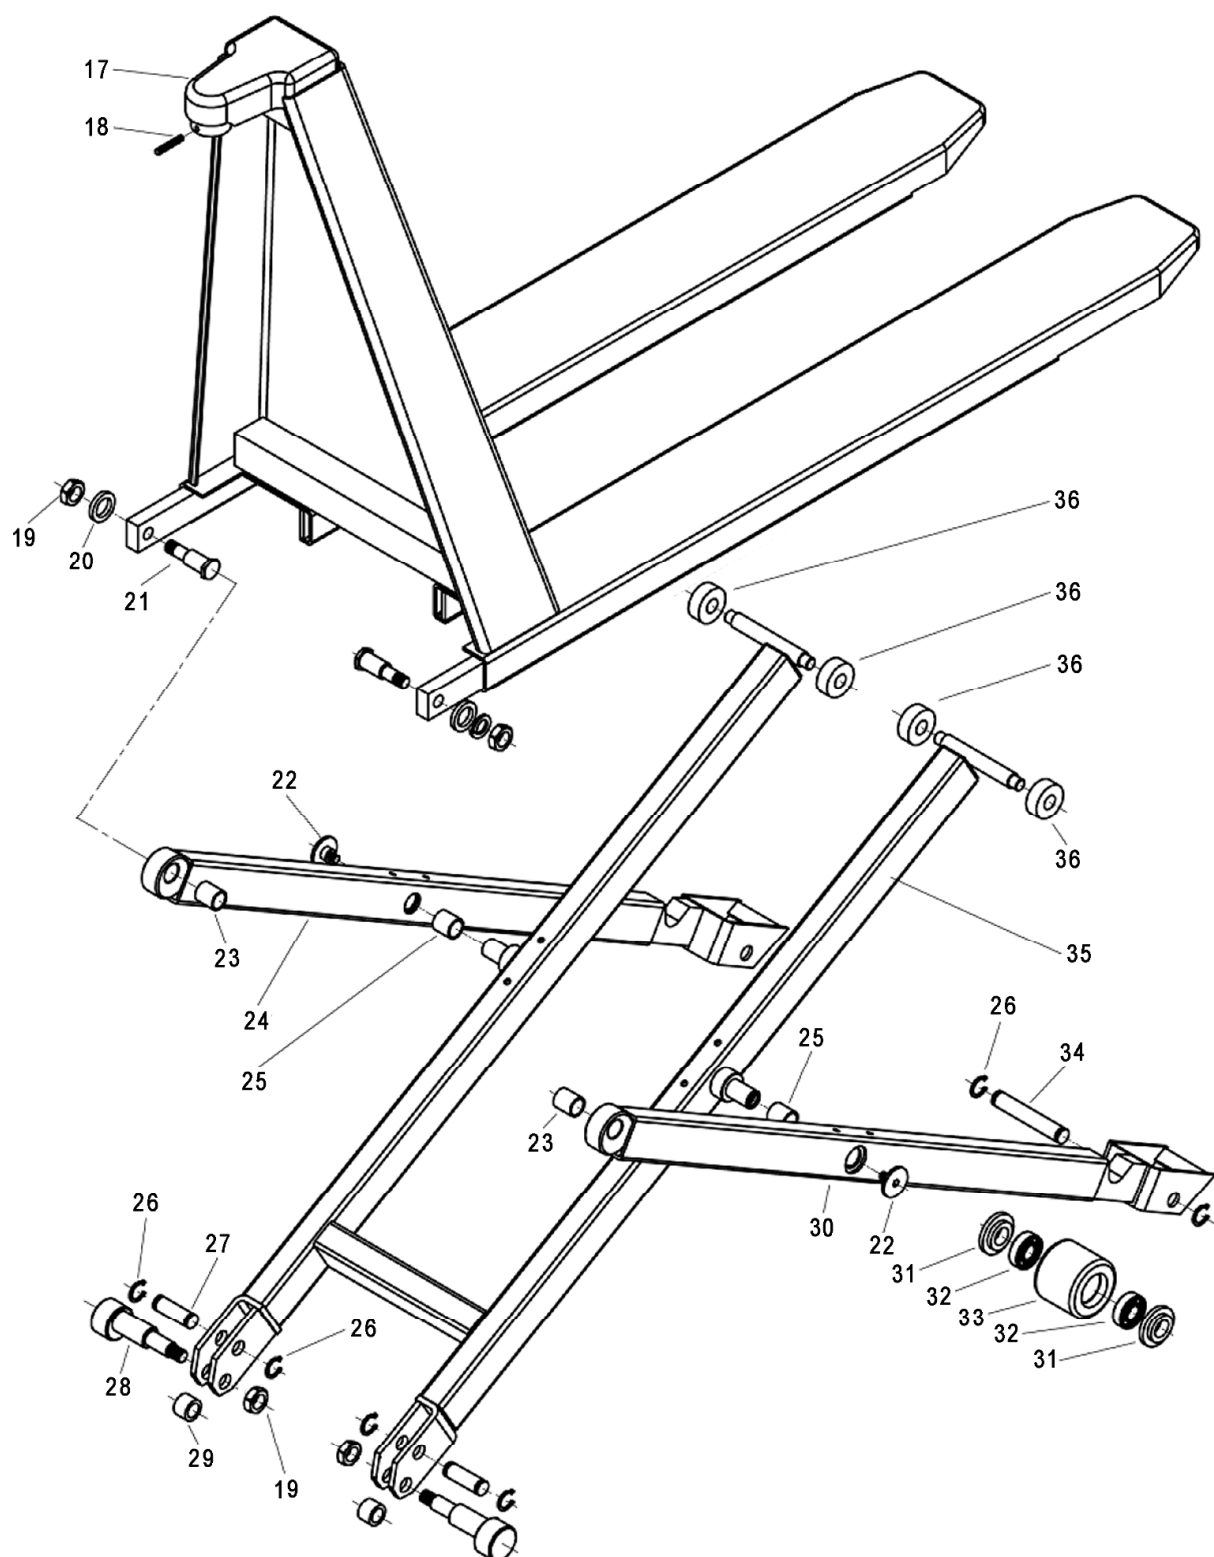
Vista explodida: chassis e mecanismo de tesoura
